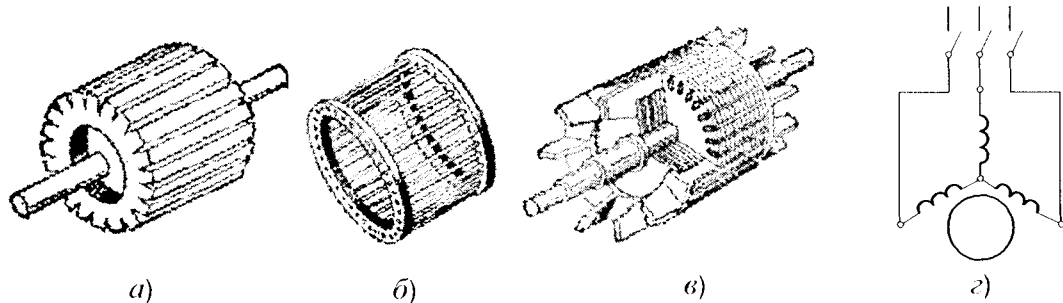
Элементы конструкции ротора: (а) - пакет ротора с валом, (б) - обмотка беличье колесо, (в) - ротор в сборе, (г) - схема включения двигателя с короткозамкнутым ротором
